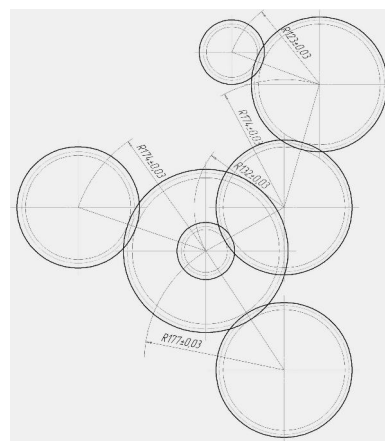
Схема механизма привода агрегатов двигателей семейства ЯМЗ-840:
